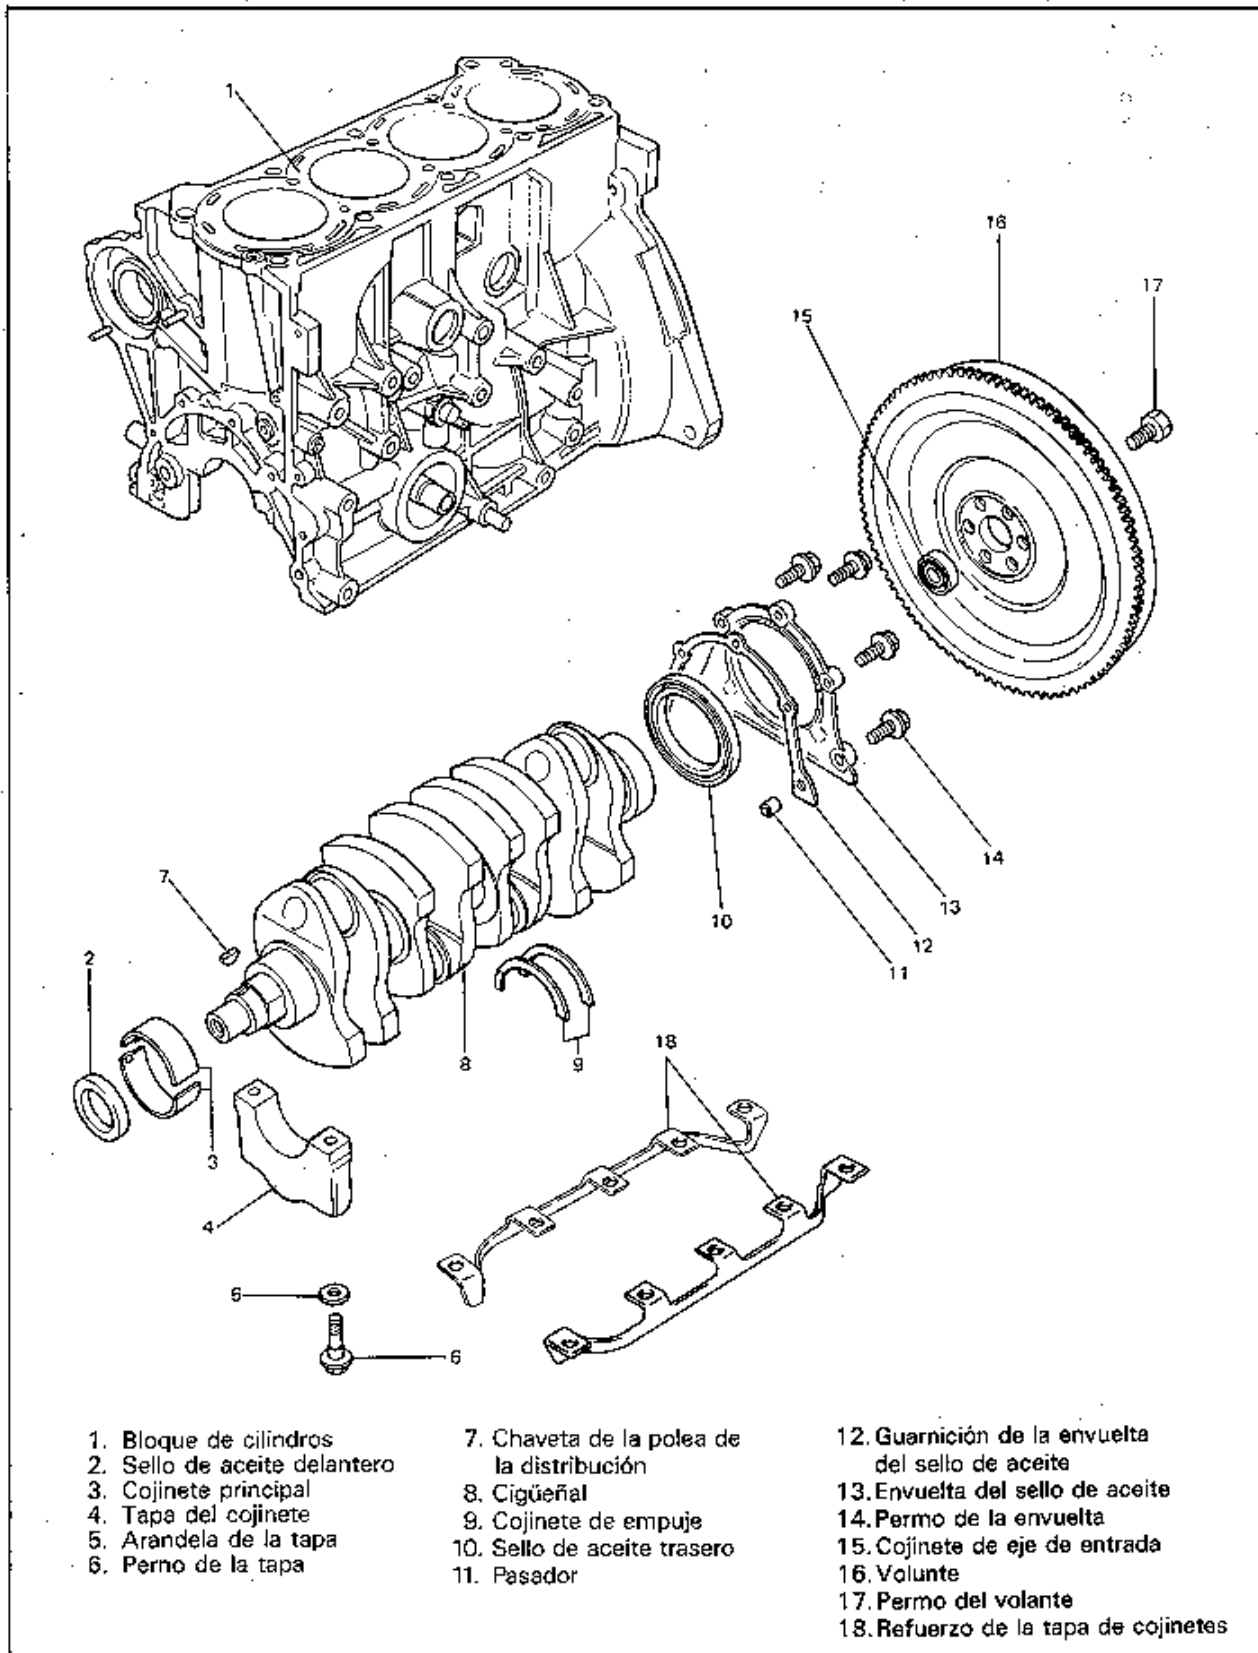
A-133 Cojinete principal, cigüeñal y bloque de cilindros
